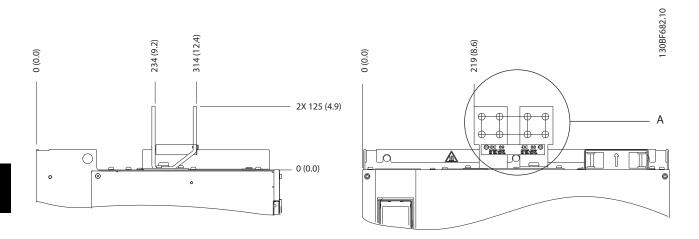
Dimensions des bornes de secteur, moteur et terre E4h (vues latérales)
